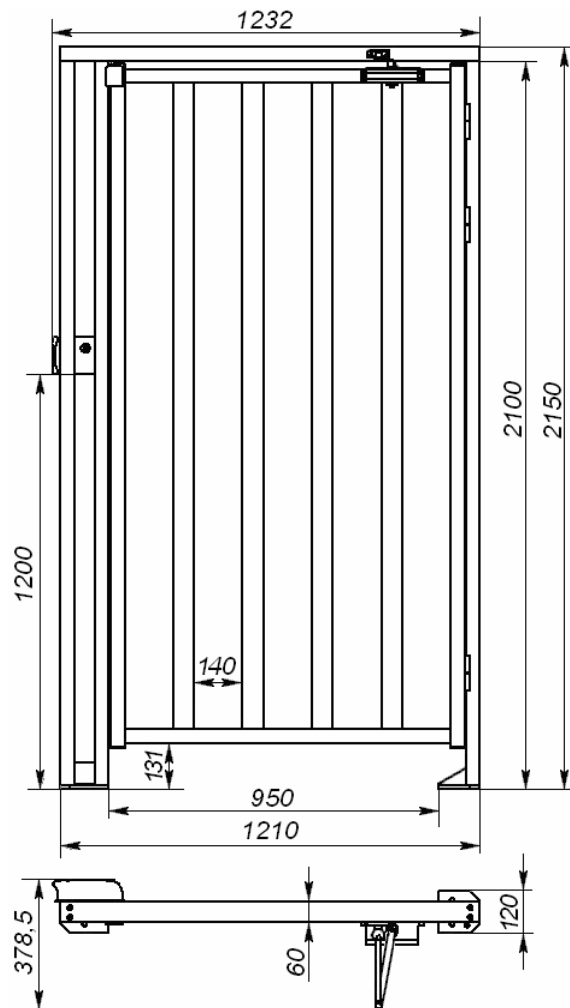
Габаритные размеры калитки PERCo-WHD-15
